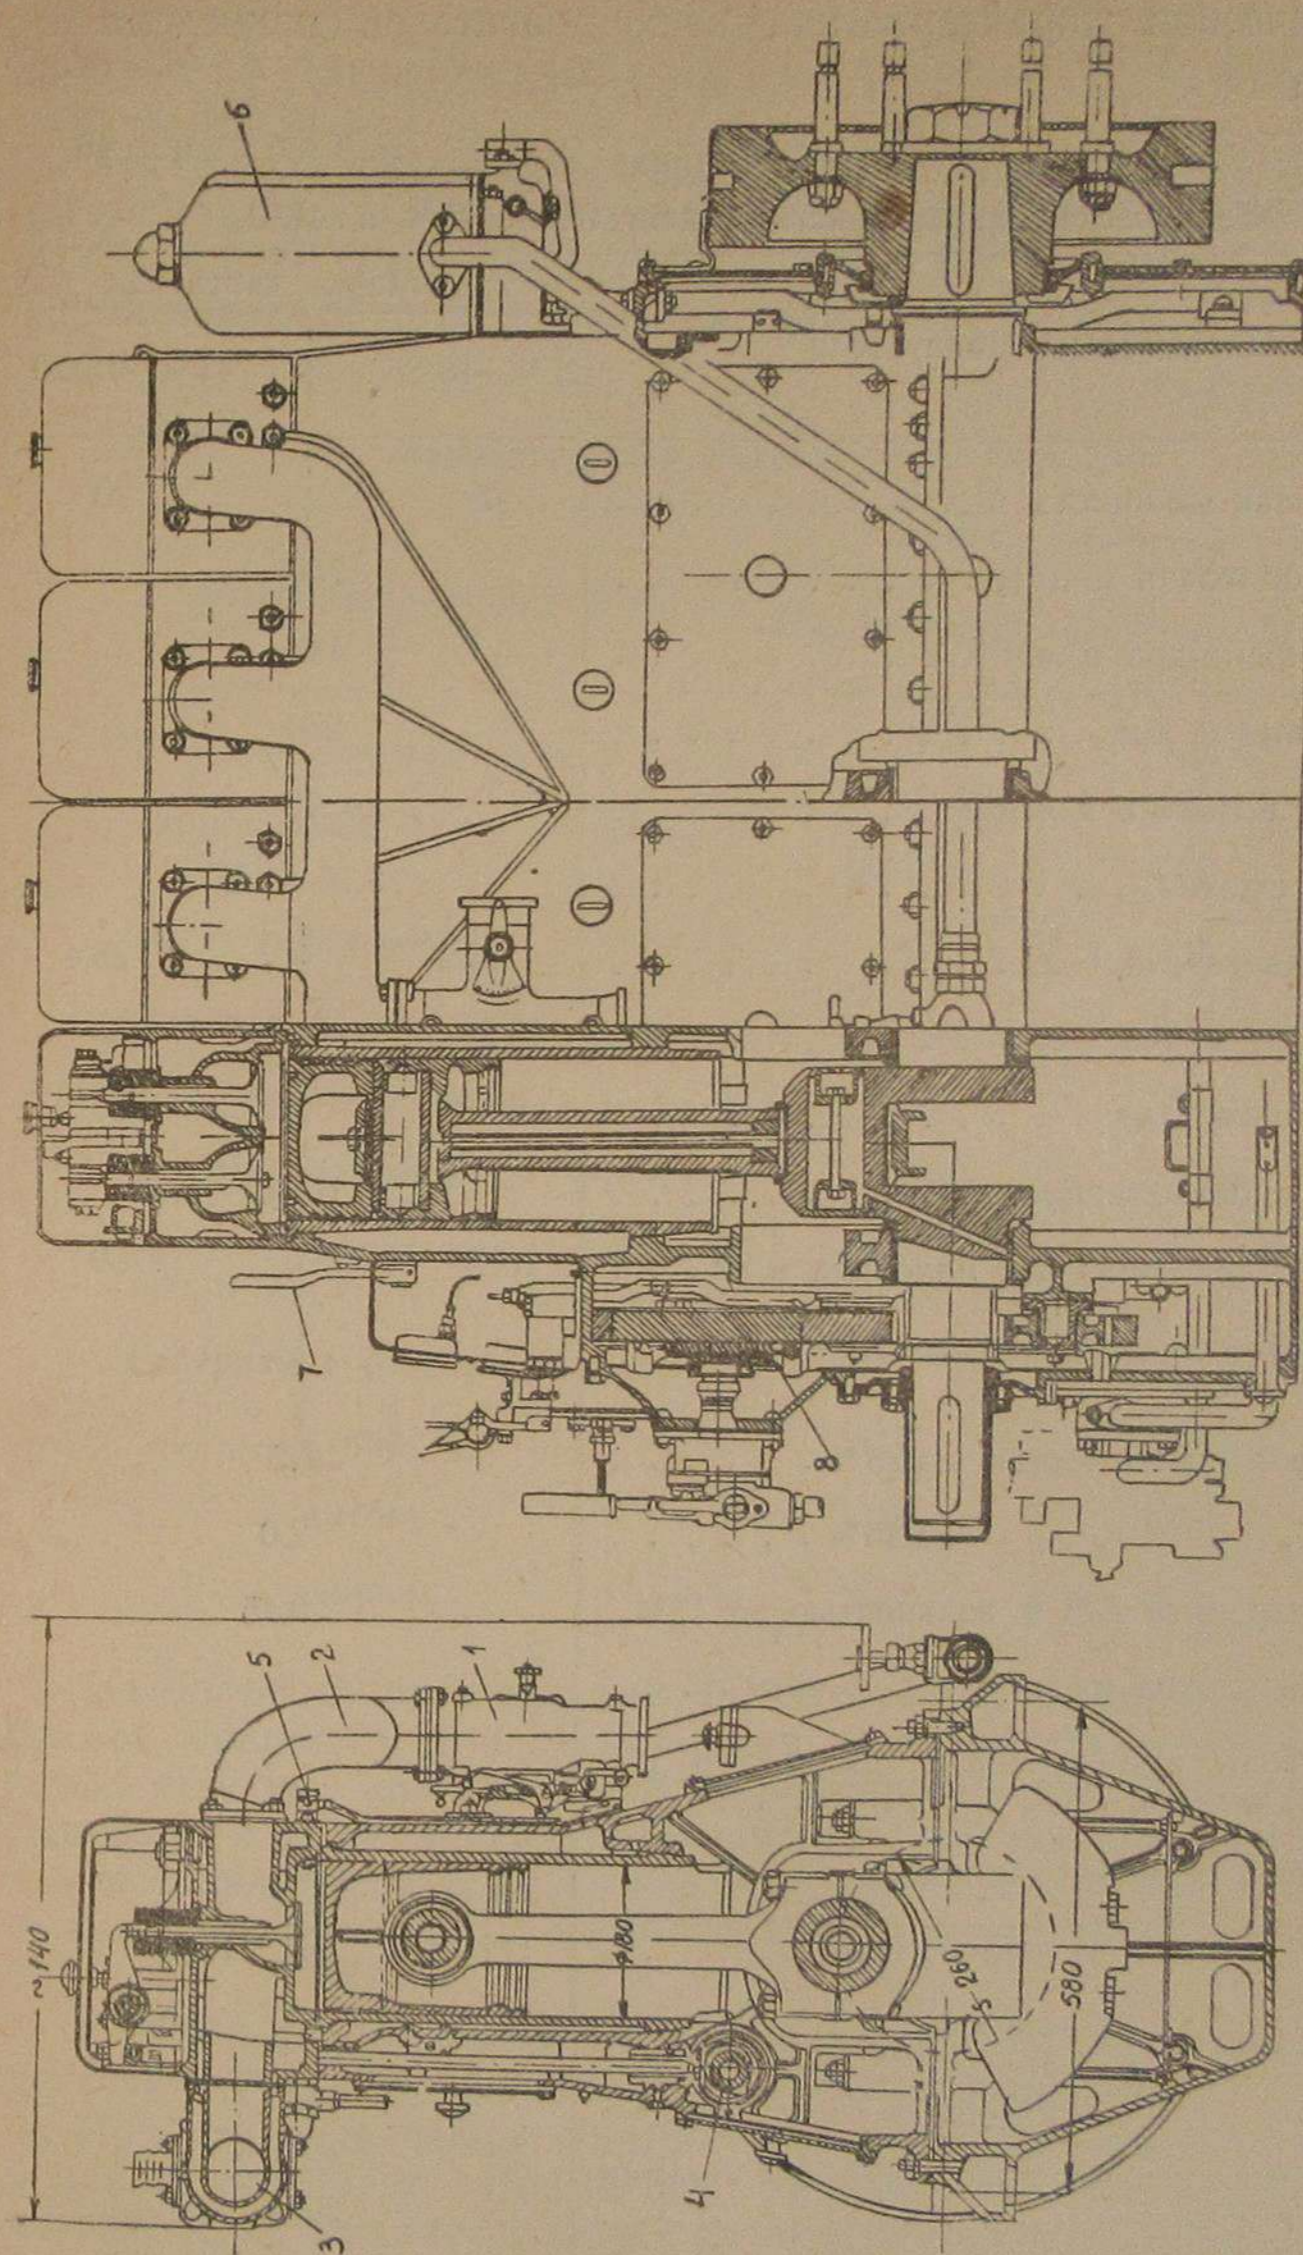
Газовый двигатель 4ГЧ 18/26:
